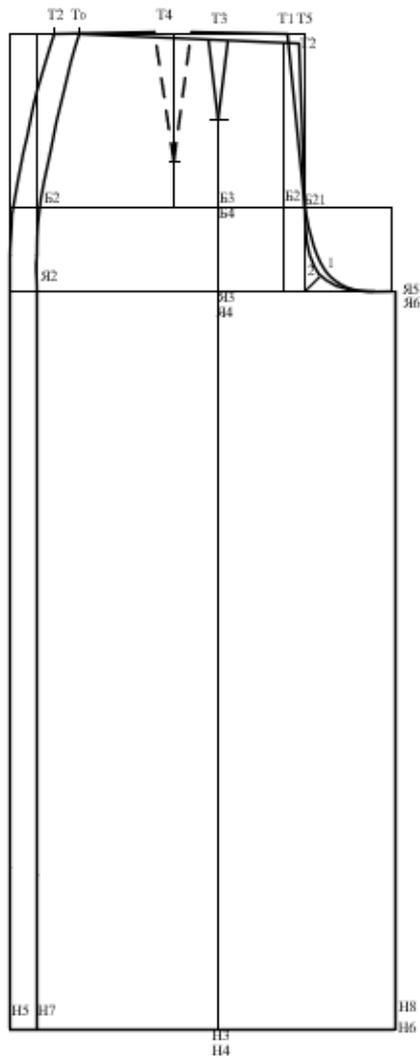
Чертеж базовой конструкции брюк (164-84-94)
